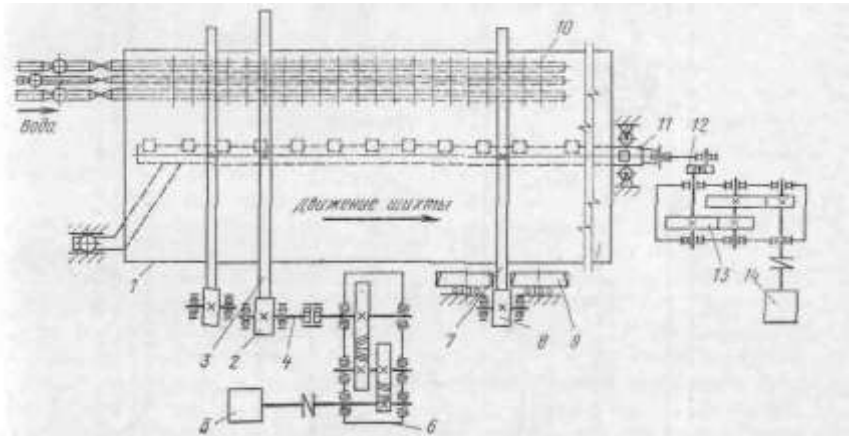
Кинематическая сема привода барабанного смесителя
